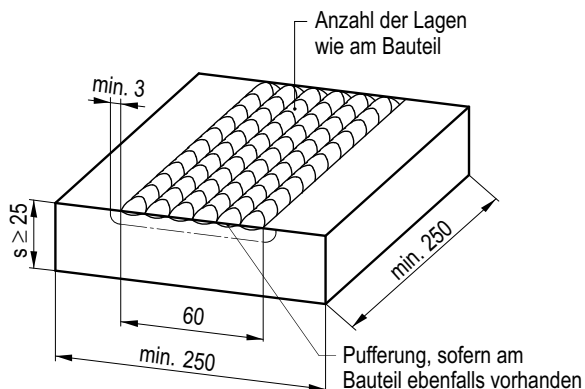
Abmessung des Prüfstücks für Hartauftragsschweißungen
